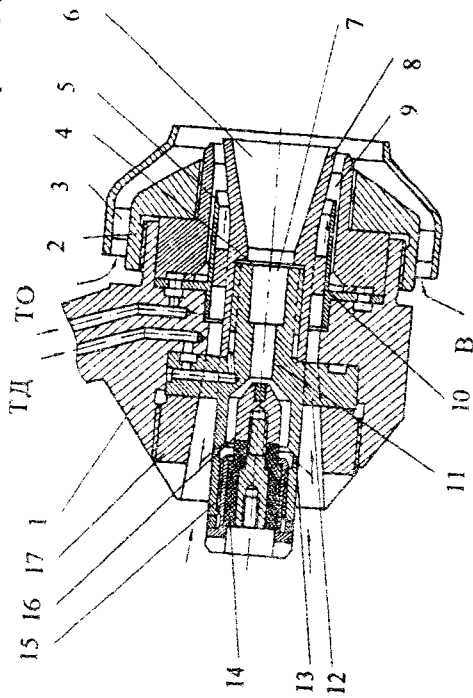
Плазменно-топливная форсунка аэрационного типа: 1,8 — корпус; 2 — гайка; 3 — завихритель; 4,5 — кольцевые щели; 6,9 — реакционная и смесительная камеры; 7 — сопло; 10 — проставка; 11 — анод; 12,13 — каналы; 14 — иригатор; 15 — корпус плазмотрона; 16 — катод; 17 — плазмотрон; В — воздух; ТО — топливо основное; ТД — топливо дополнительное
